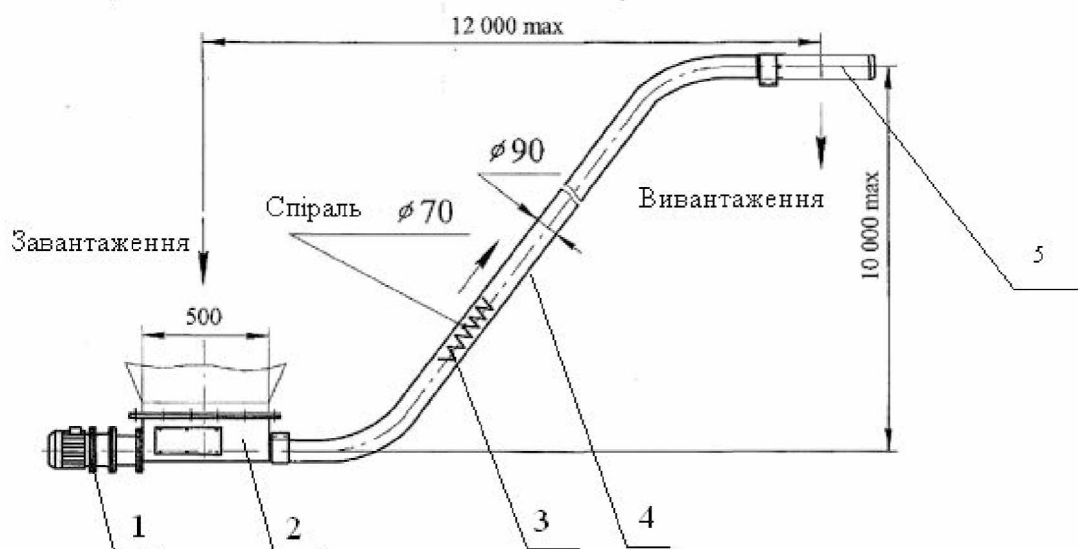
Схема спіроматика: 1 – мотор-редуктор; 2 – завантажувальний патрубок; 3 – спіраль; 4 – трубопровід; 5 – вивантажувальний патрубок.
